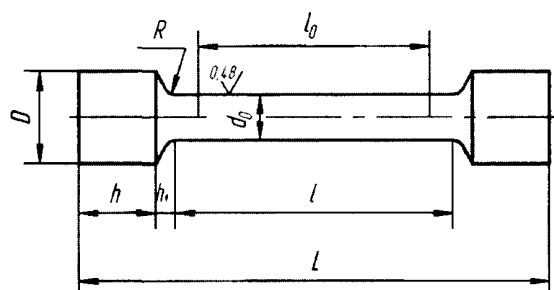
Образец для испытания металла шва на статическое растяжение
